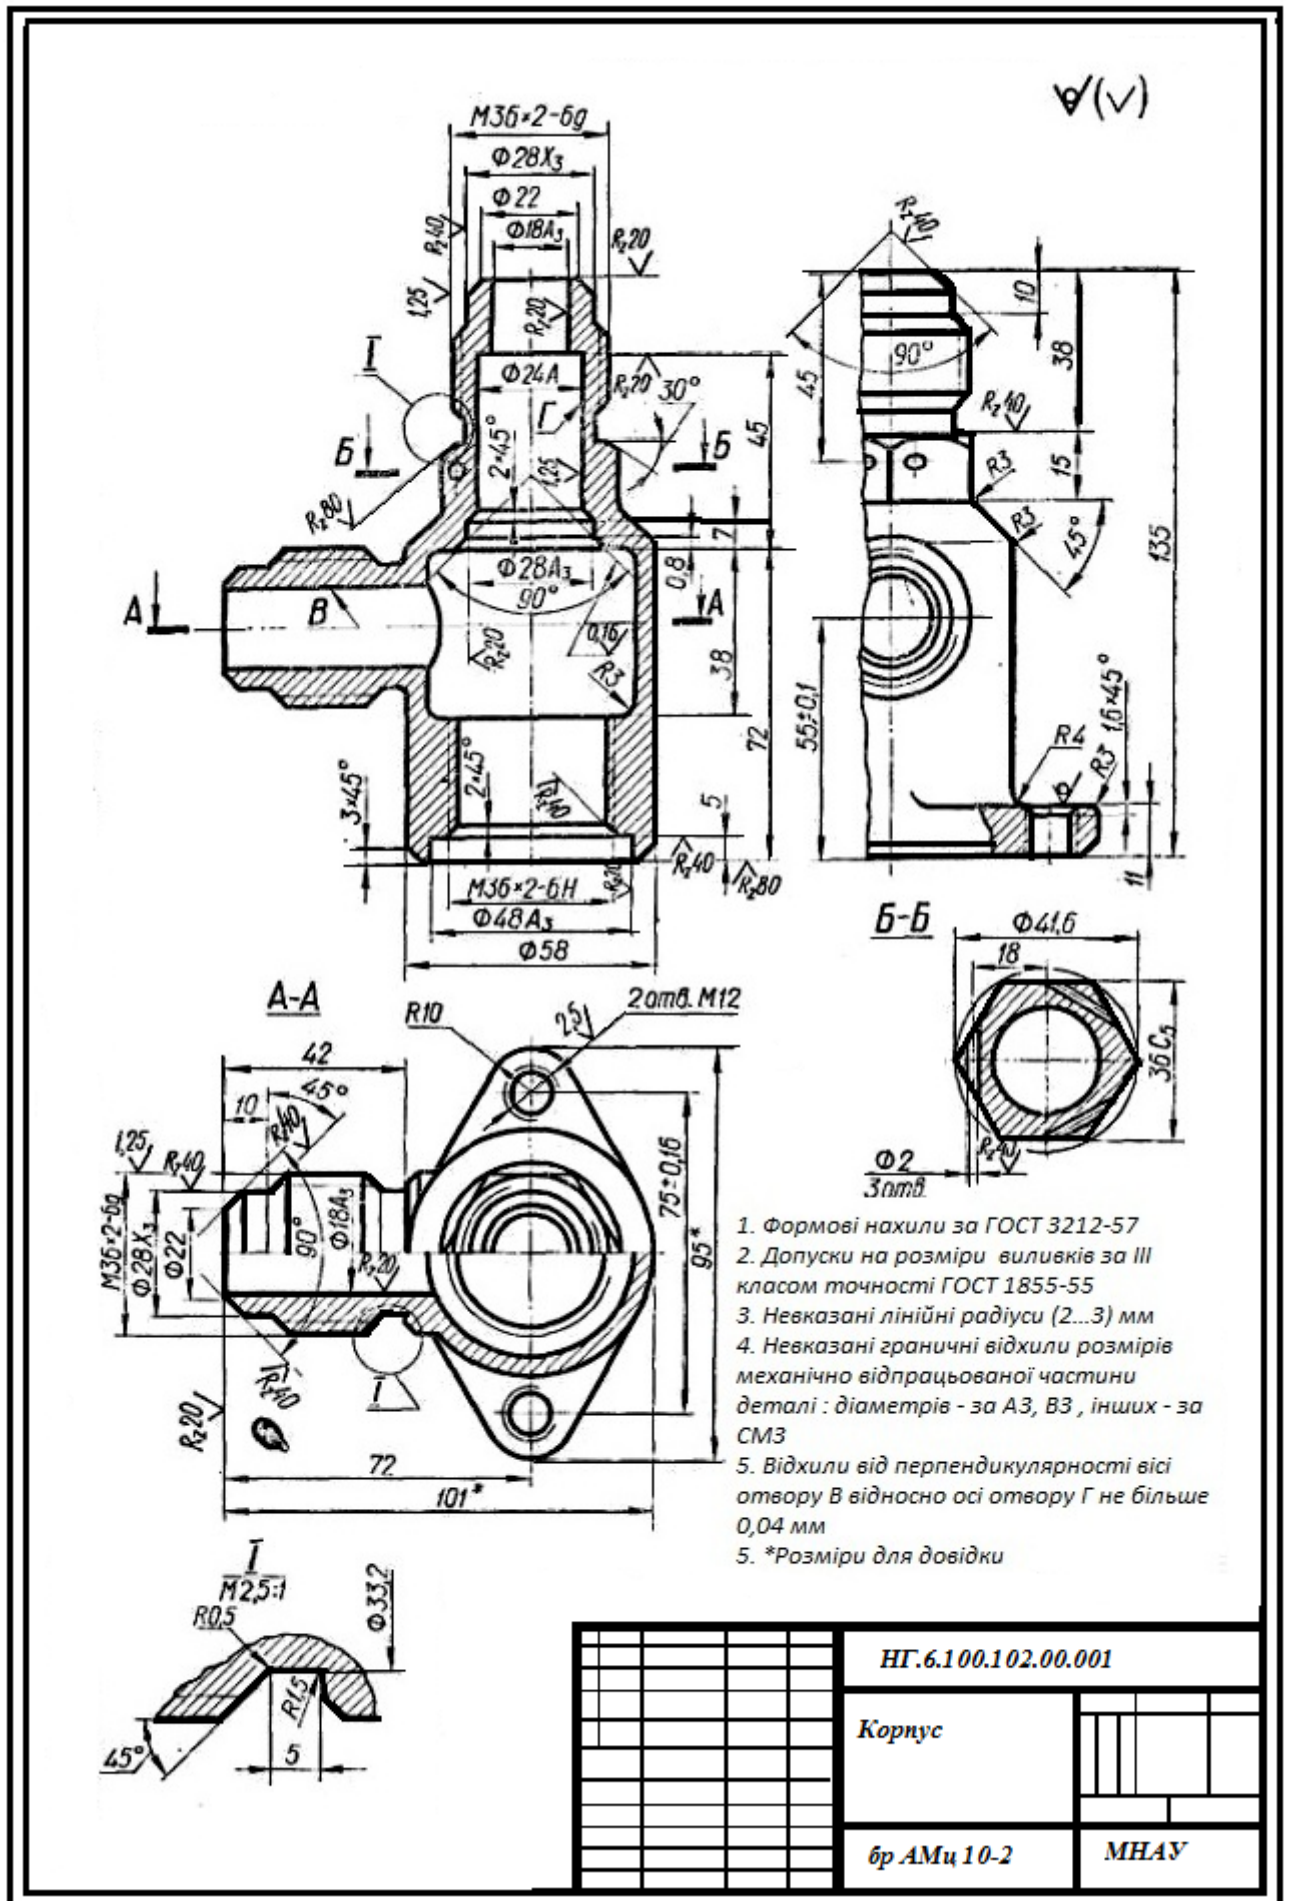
Робоче креслення деталі подвійного зворотного клапана
